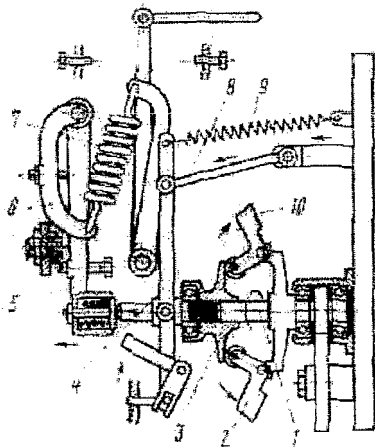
Схема работы регулятора при увеличении частоты вращения коленчатого вала: 1 - валик регулятора; 2, 10 - грузы; 3 - муфта; 4 - рычаг привода рейки; 5 - рычаг ручного привода; 6 - двуплечий рычаг; 7 - пружина регулятора; 8 - тяга рейки; 9 - пружина рычага рейки
